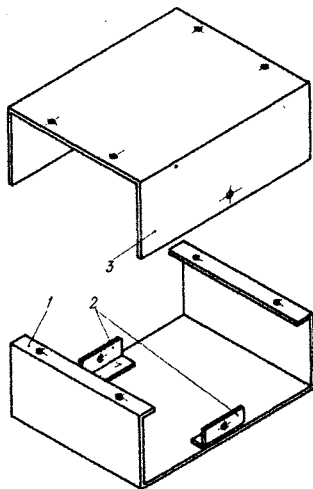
Корпус из двух П-образных деталей: 1 — основание; 2 — уголок, 2 шт., закрепить на дет. 1 заклепками; 3 — крышка.
